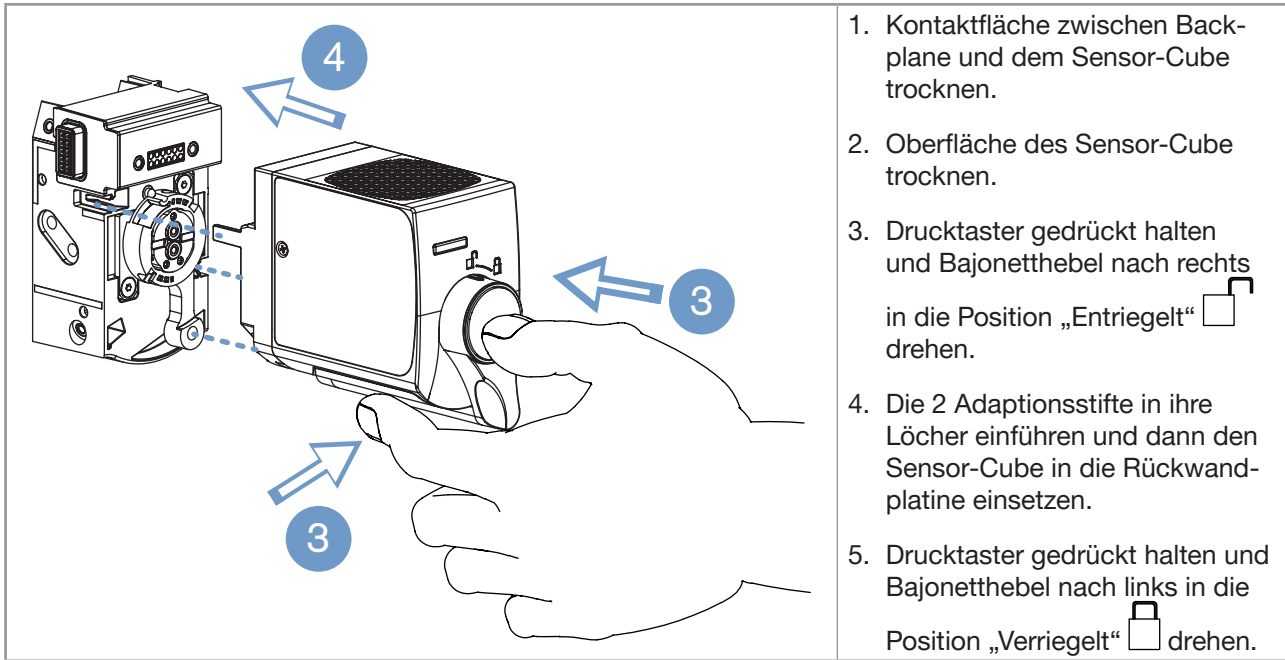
Montage des Sensor-Cube auf der Backplane des Systems
